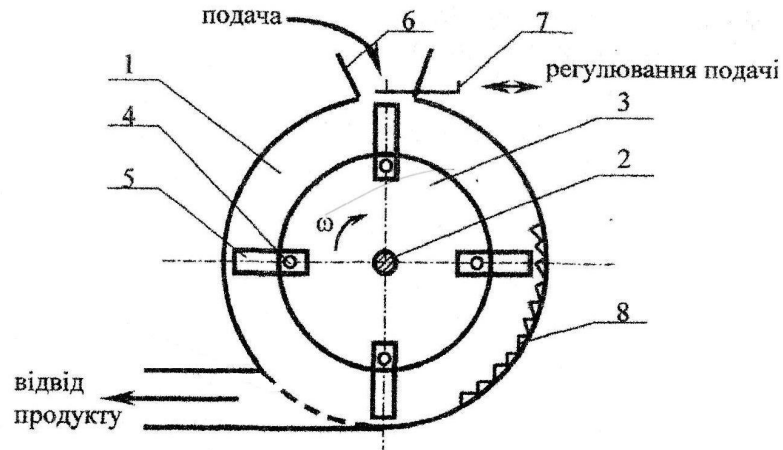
Схема молоткової дробарки кормів: 1- дробильна камера ; 2- вал; 3- диск; 4- палець; 5- молоток; 6- завантажувальна горловина; 7- дозатор подачі; 8- решето.
